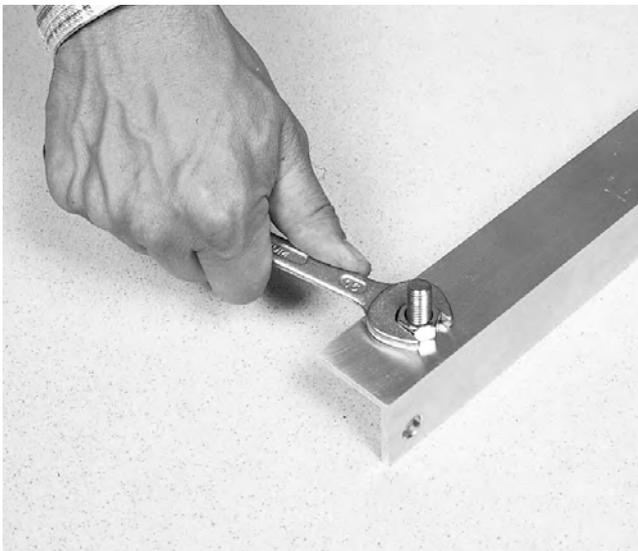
Fixez maintenant sur chaque profilé (pièce 1 Fig. 2,3 ou 4) deux vis M10x30. Vissez l'écrou de manière à ce que son flanc soit perpendiculaire au côté large du profilé. (Clé de 16)
